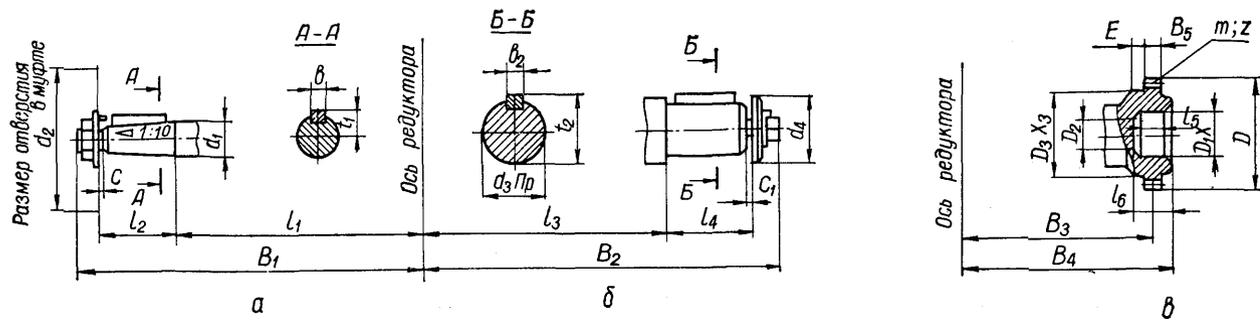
Присоединительные размеры концов валов редукторов РМ:
